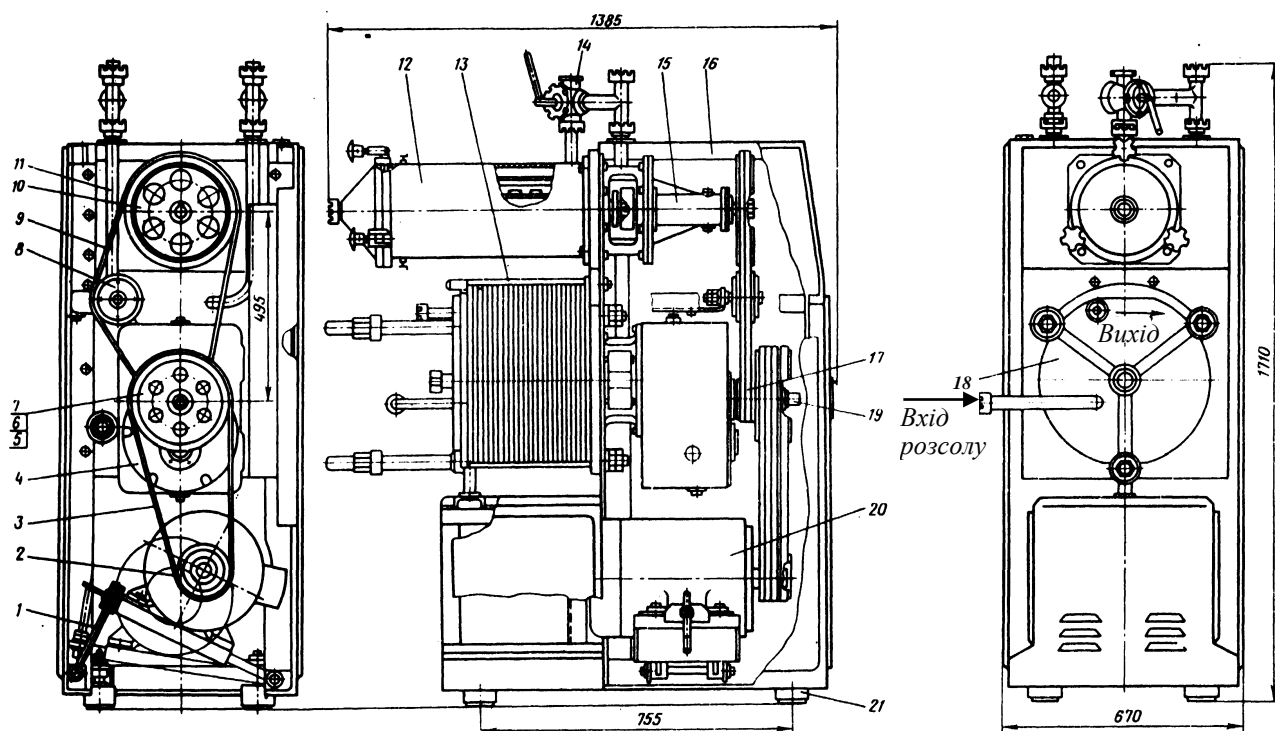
Загальний вид маслоутворювача марки РЗ-ОУА:
